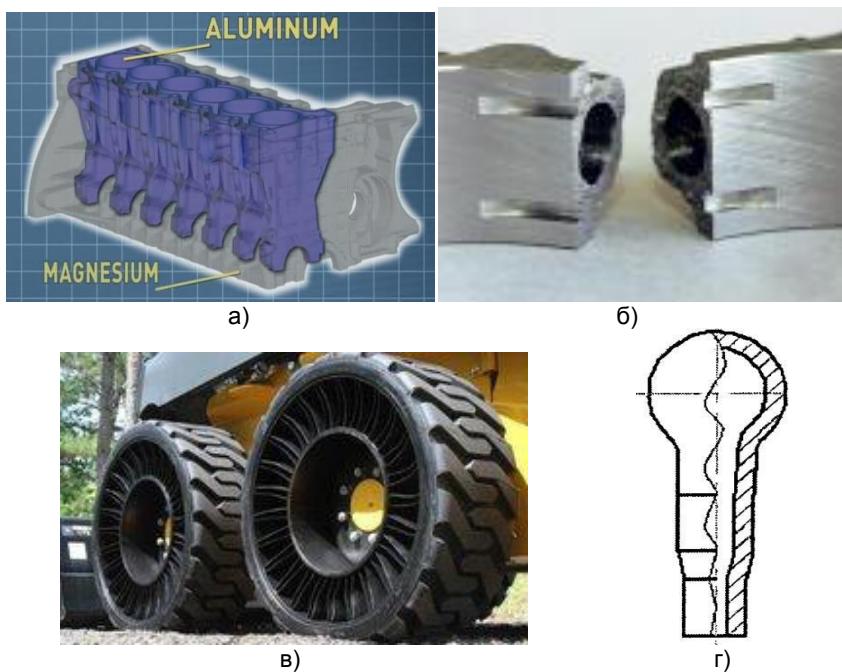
Отливка блока двигателя BMW (а); слом шатуна для последующей сборки без смещения разобщенных частей (б); колеса фирмы Michelin с безвоздушными шинами (в); шаровый палец полый (г)
